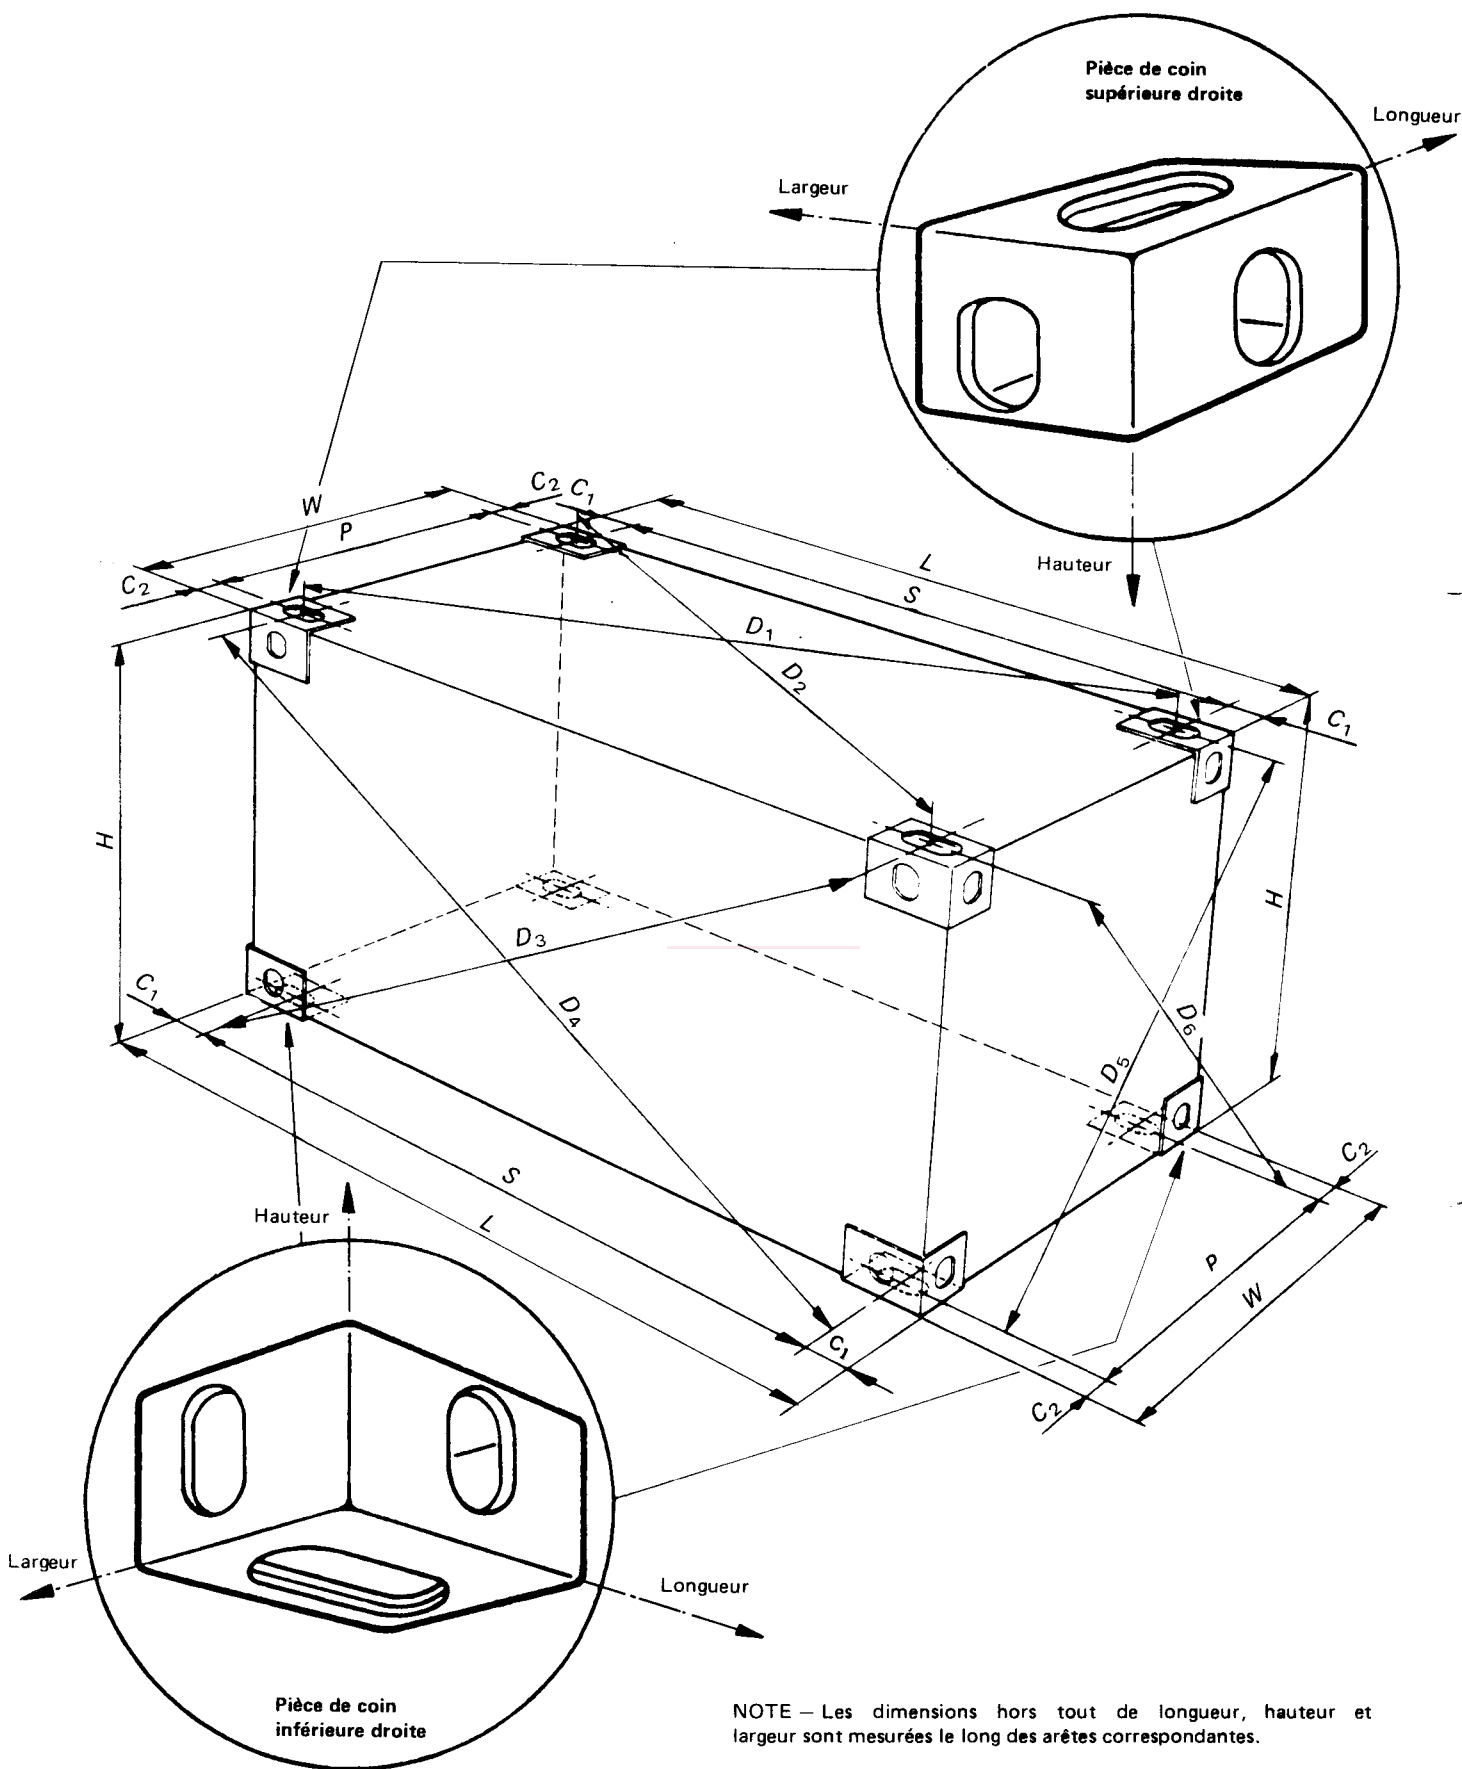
Position des pièces de coin — Tolérances sur les dimensions diagonales (voir tableau)
